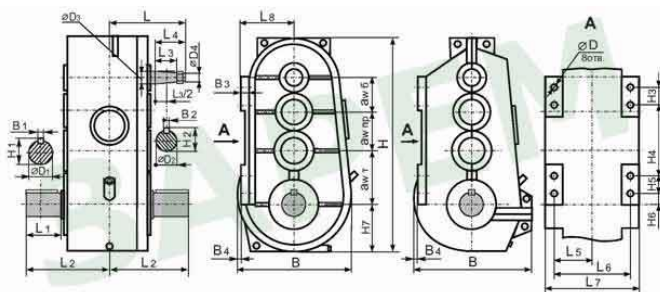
Редуктор циліндричний вертикальний трьохступеневий типу ВКУ-М
